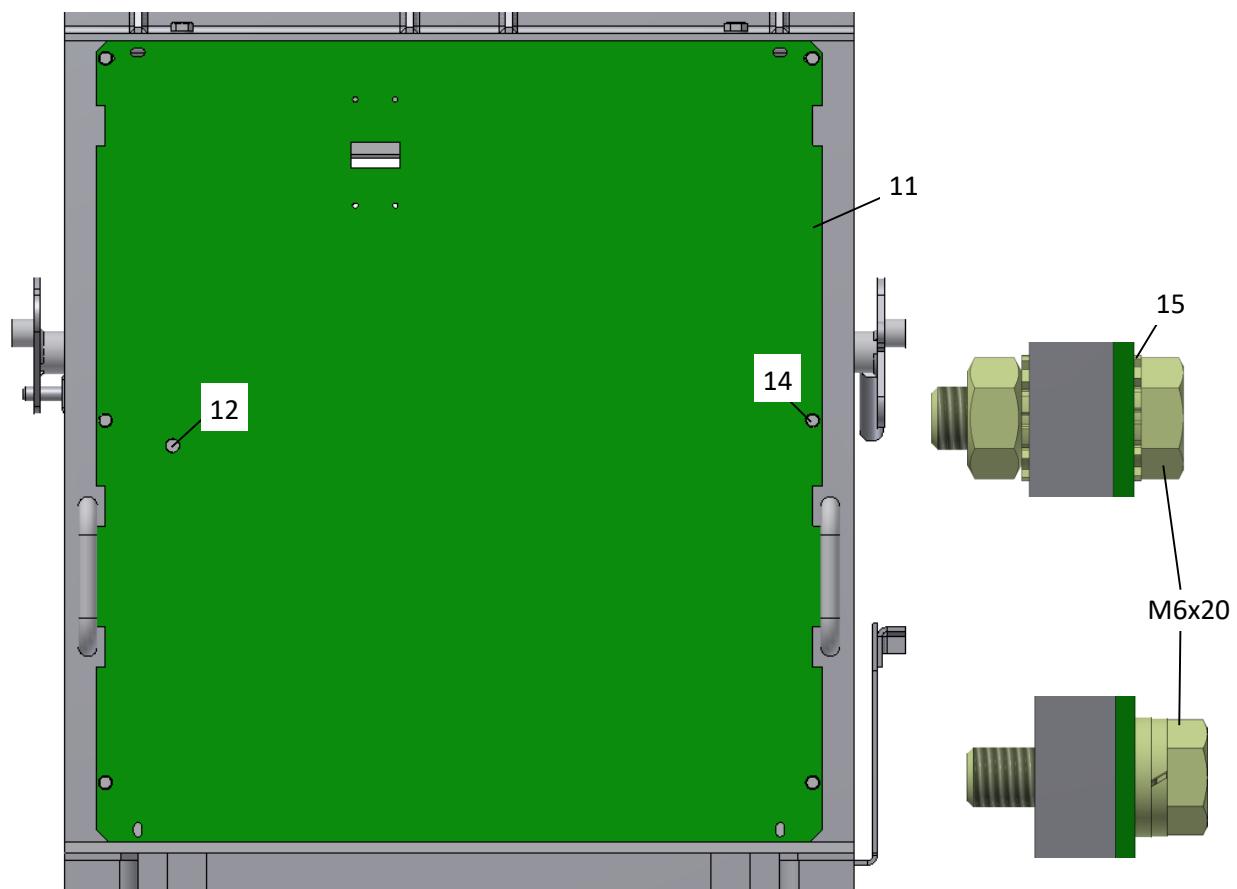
Установка фасадного листа на раму ВМПЭ-10 шириной 210 мм
